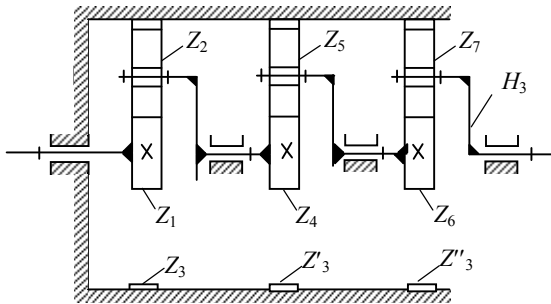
Зубчатый механизм, составленный из трех планетарных ступеней
